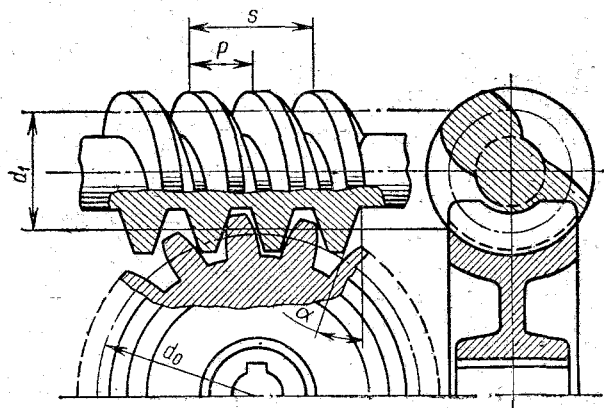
Общий вид червячной передачи с двухзаходным червяком
